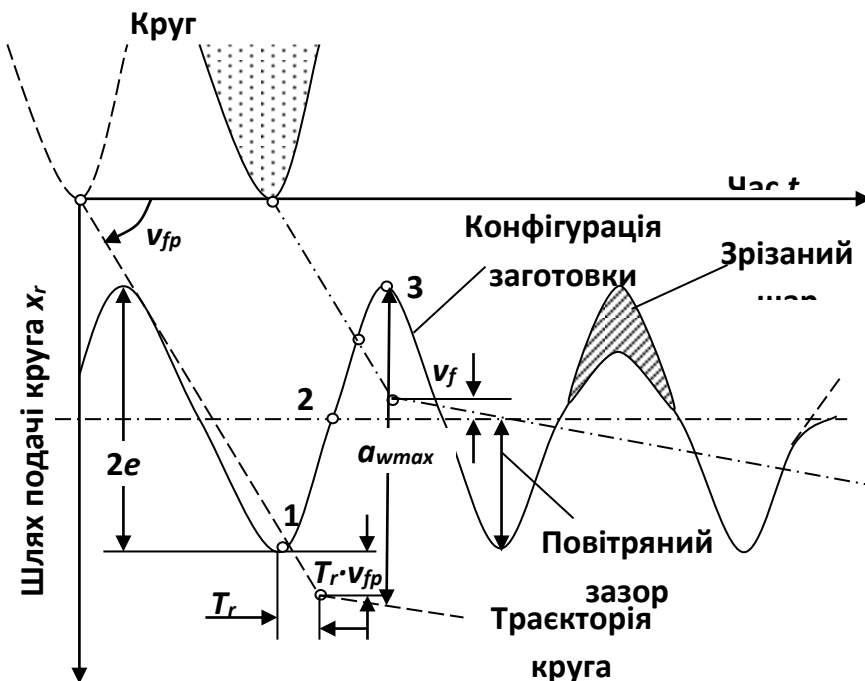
Перший контакт круга із заготовкою з ексцентриситетом e
